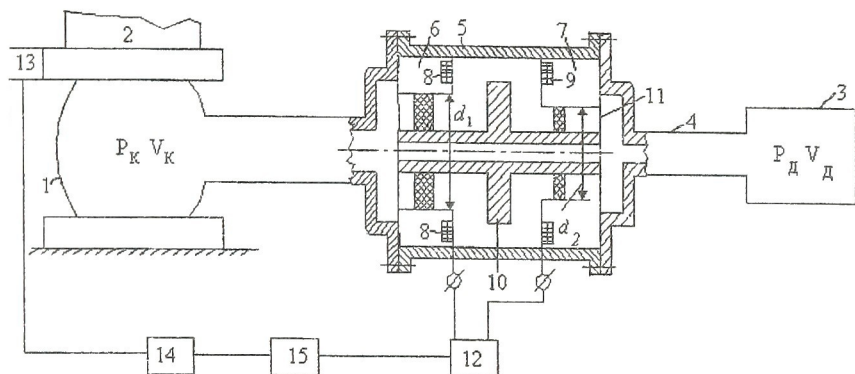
Конструктивная схема пневматического виброизолятора
